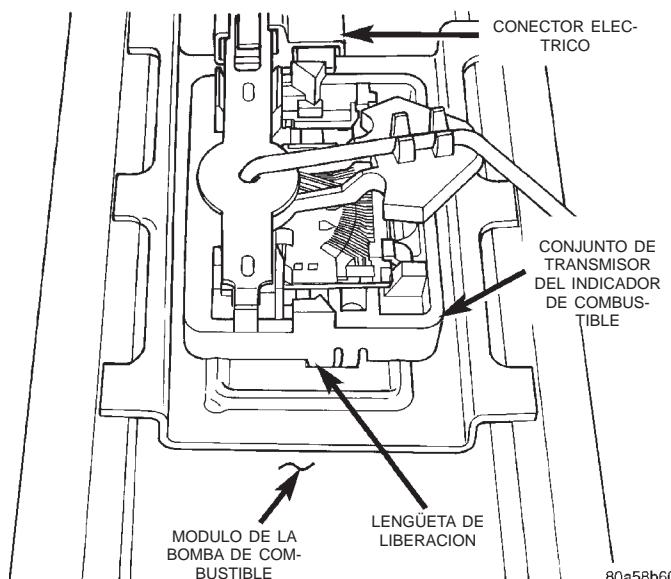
Lengüeta de liberación del conjunto de transmisor del indicador de combustible
